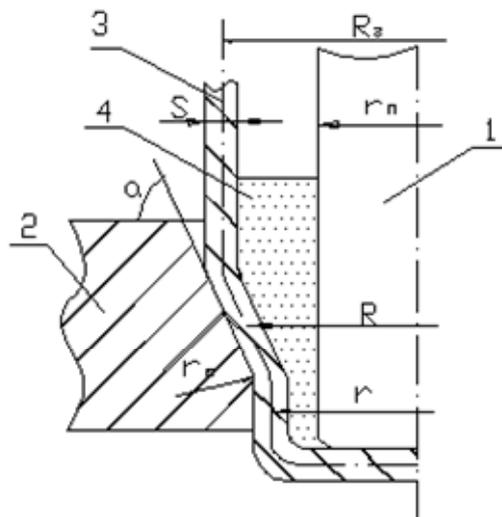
Схема вытяжки втулки подшипника: 1 – пуансон; 2 – матрица;
